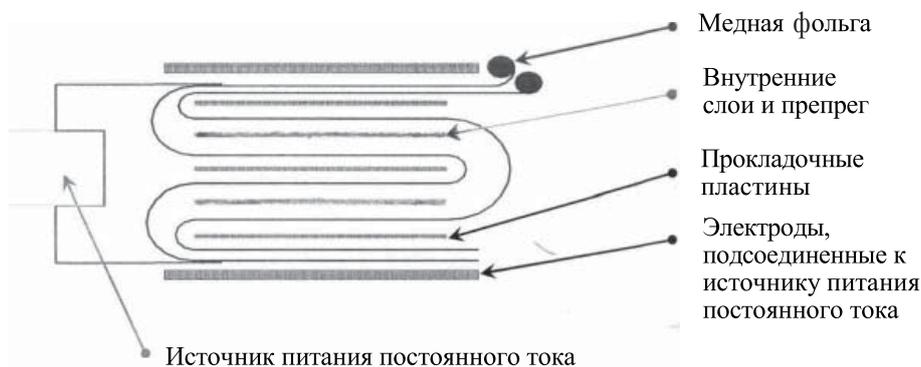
Схема сборки пресс-пакета в системе ADARA
